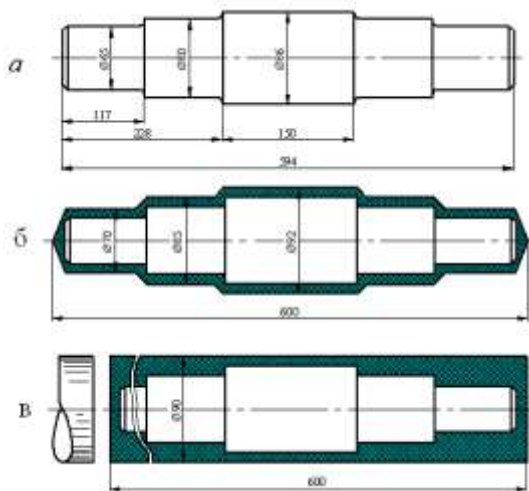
Вал ступінчастий: а – деталь; б – штампована поковка; в – заготовка з гарячекатаного прокату
